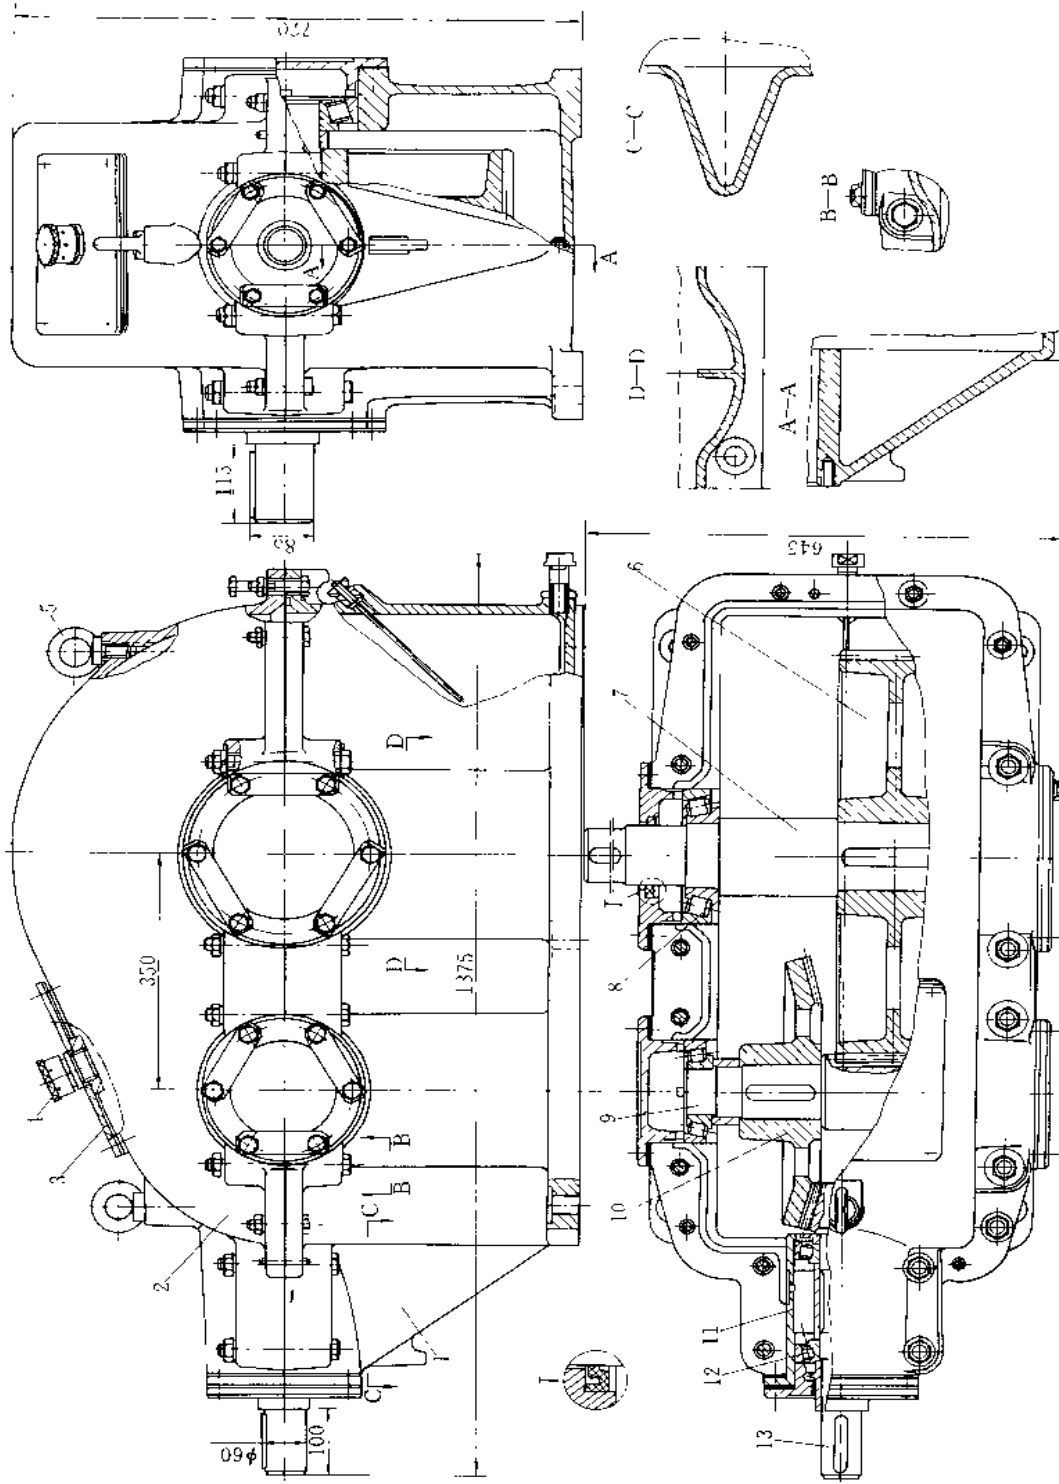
两级圆锥-圆柱齿轮减速器
